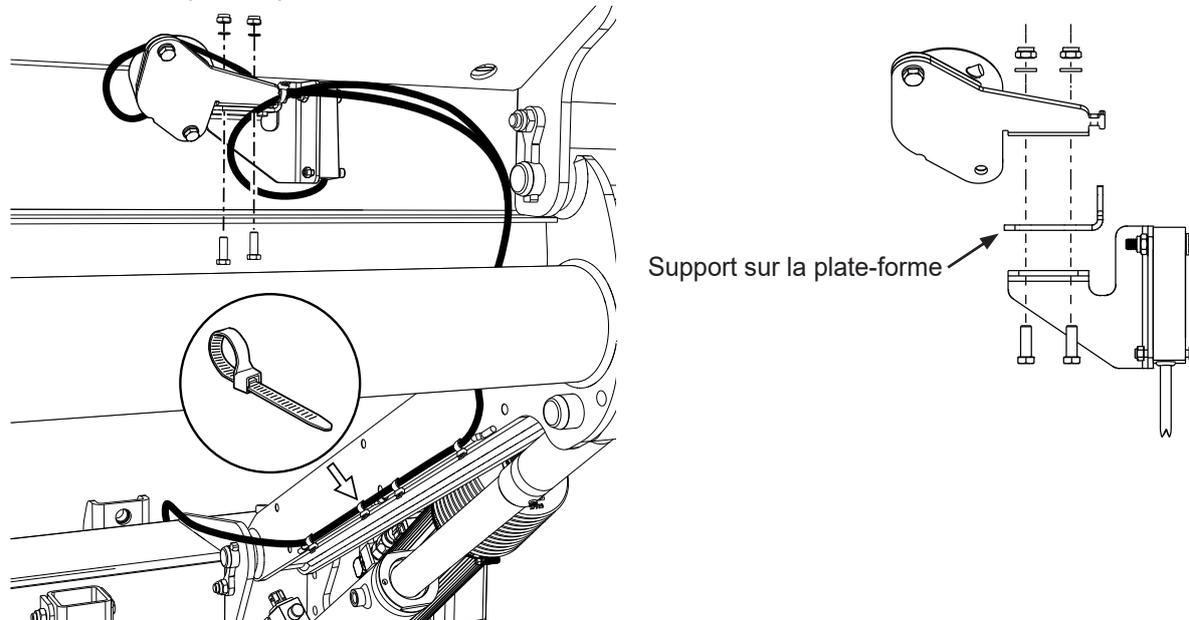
Capteur d'angle de montage pour ouverture / fermeture automatique
